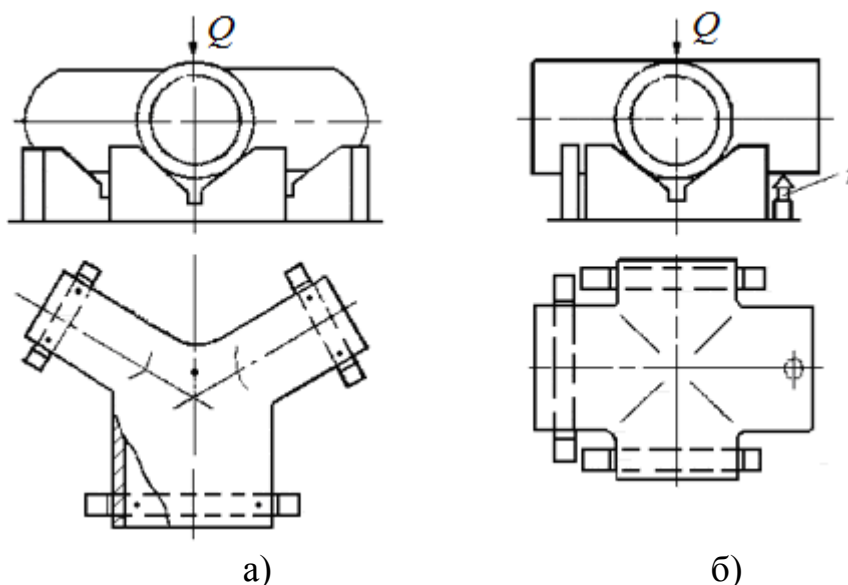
Схеми установлення заготовок типу трійників та хрестовин
